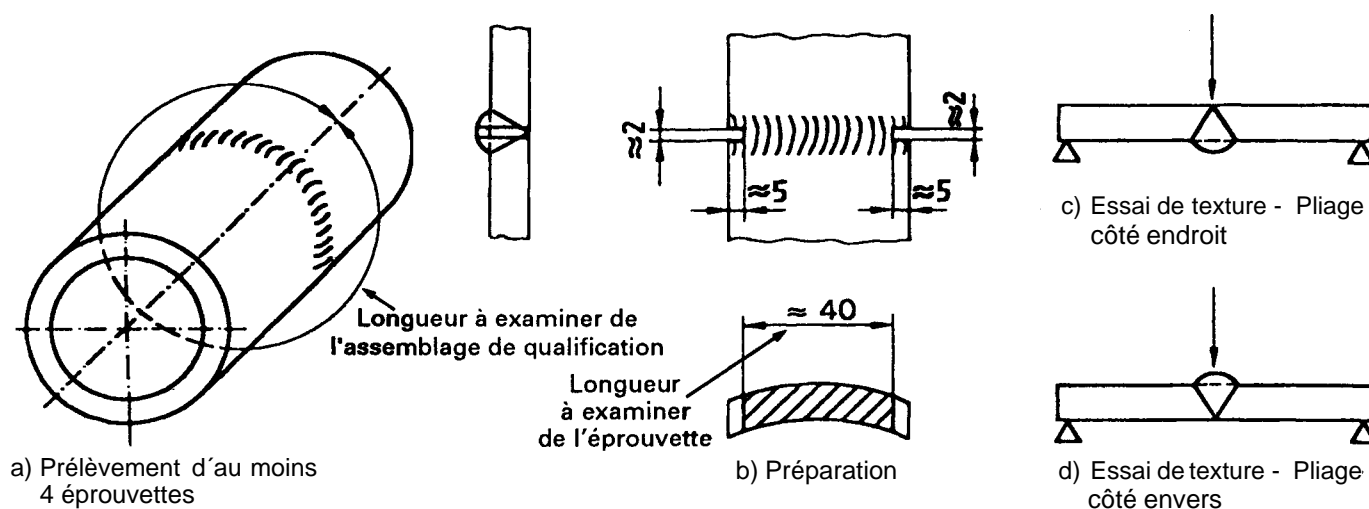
Préparation et essai des éprouvettes de texture d'assemblage de qualification bout à bout de tubes (Dimensions en mm)
